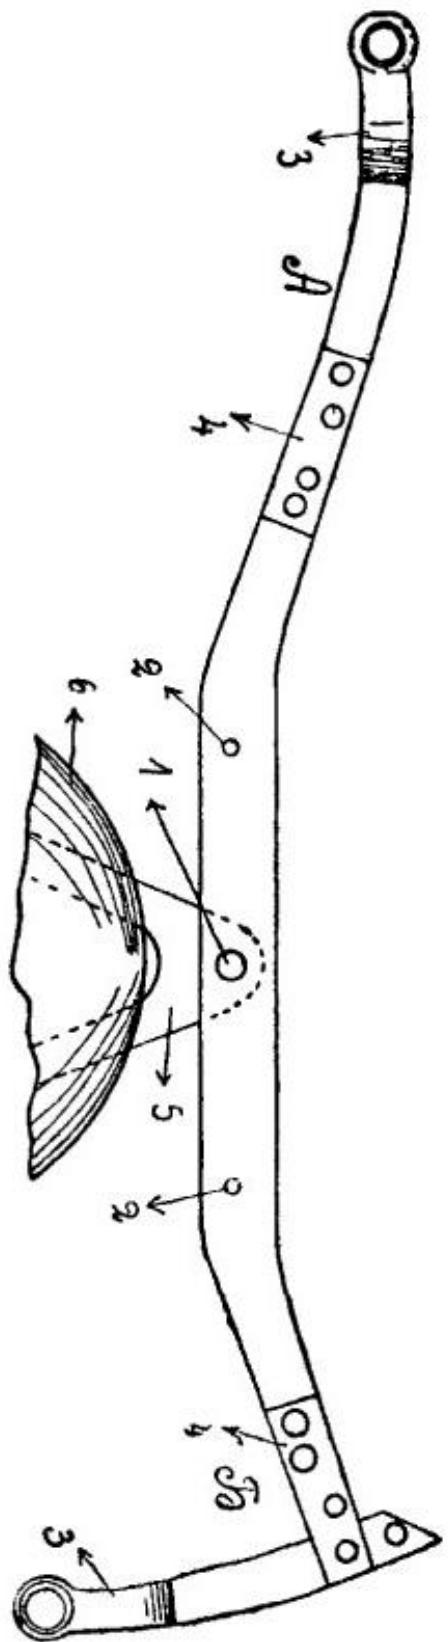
Складывающееся вниз коромысло. А — вид откинутого коромысла, Б — вид сложенного коромысла, 1 — осевое отверстие, 2 — поршневые отверстия, 3 — ухват коромысла, 4 — накладки, 5 — стойки трубы, 6 — верхушка воздушного колпака трубы.
